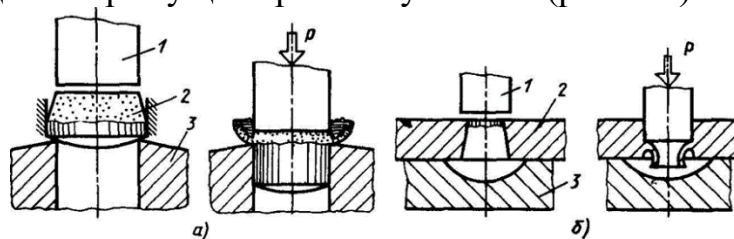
Схема зачистной штамповки внешнего (а) и внутреннего (б) контура детали:
